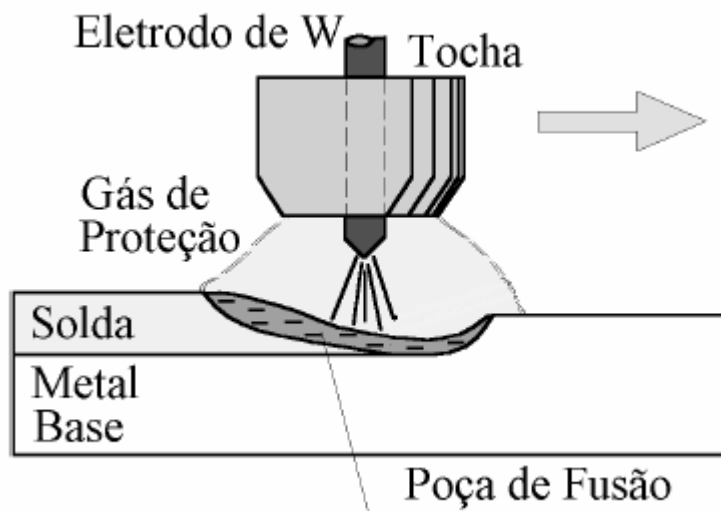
Processo de soldagem TIG (Marques, 1991).
